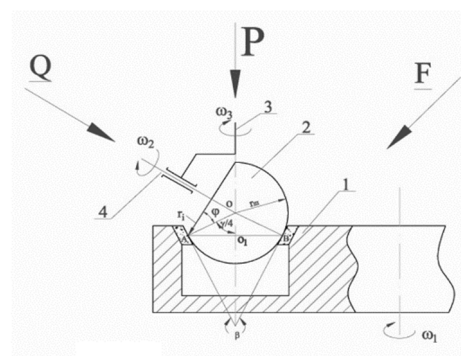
Кинематическая схема формообразования неполной сферической поверхности торцевым шлифованием на основе способа НПШ: 1 – торцевой шлифовальный круг; 2 – обрабатываемая деталь – неполная сфера; 3 – ось вращения шпинделя детали; 4 – ось вращения детали
